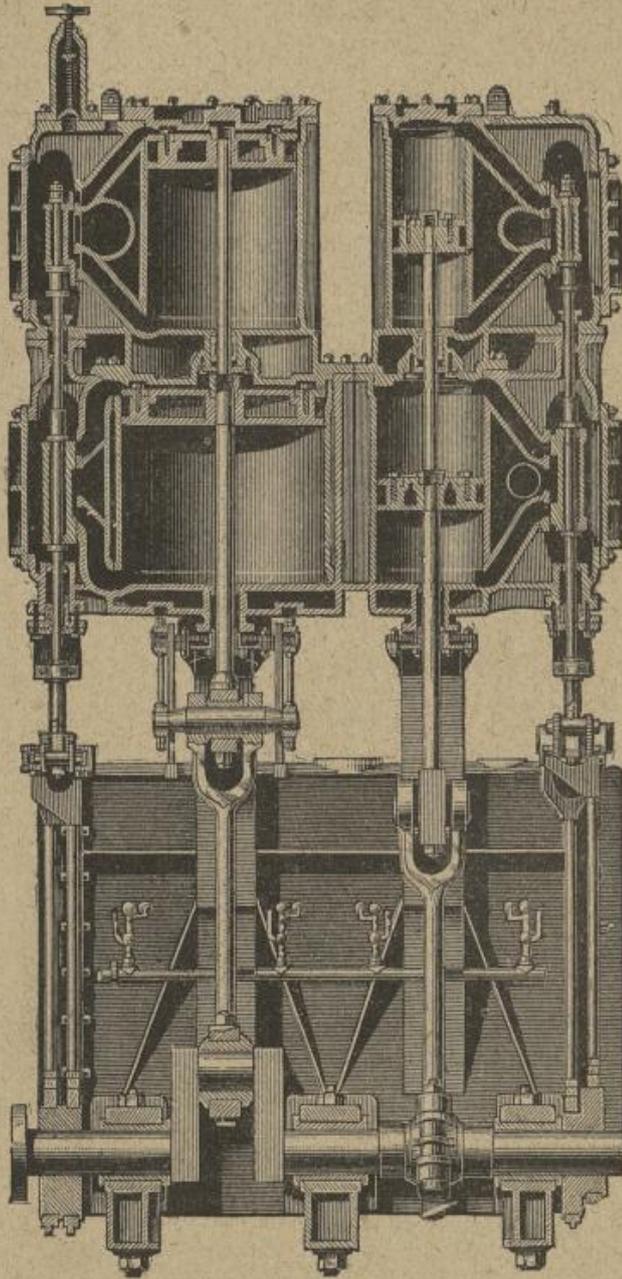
Machine à quadruple expansion, à deux manivelles
